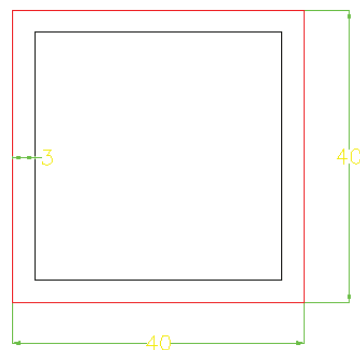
27 Junta de soldadura de filete de la viga AB
